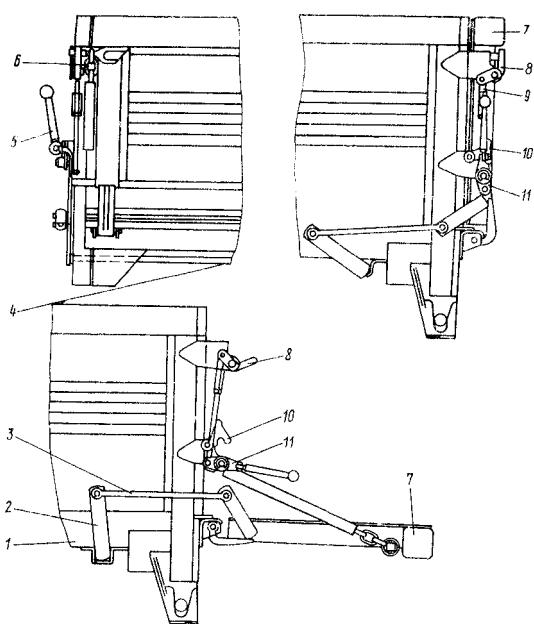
Механизм запора бортов платформы автомобиля КамАЗ-55502: 1 - борт боковой; 2 - рычаг торсиона; 3 - тяга торсиона; 4 - торсион; 5 - рукоятка рычага механизма запора; 6 - цепь; 7 - борт задний; 8 - крюк запора бокового борта; 9 - тяга верхняя; 10 - фиксатор; 11 - рычаг механизма запора
